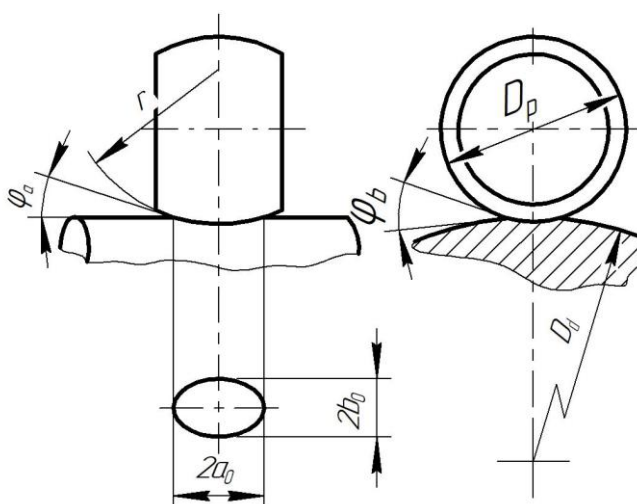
Форма відбитка ролика на оброблюваній поверхні деталі при обкатуванні
